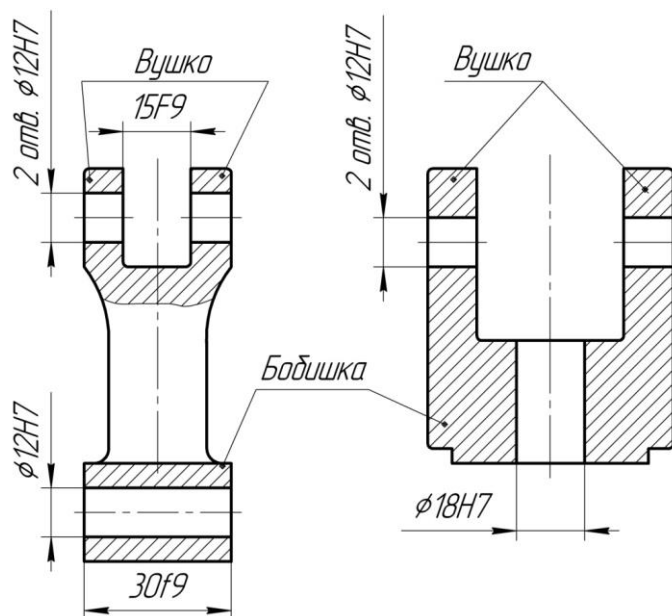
Креслення двох вилок шарнірного з'єднання
